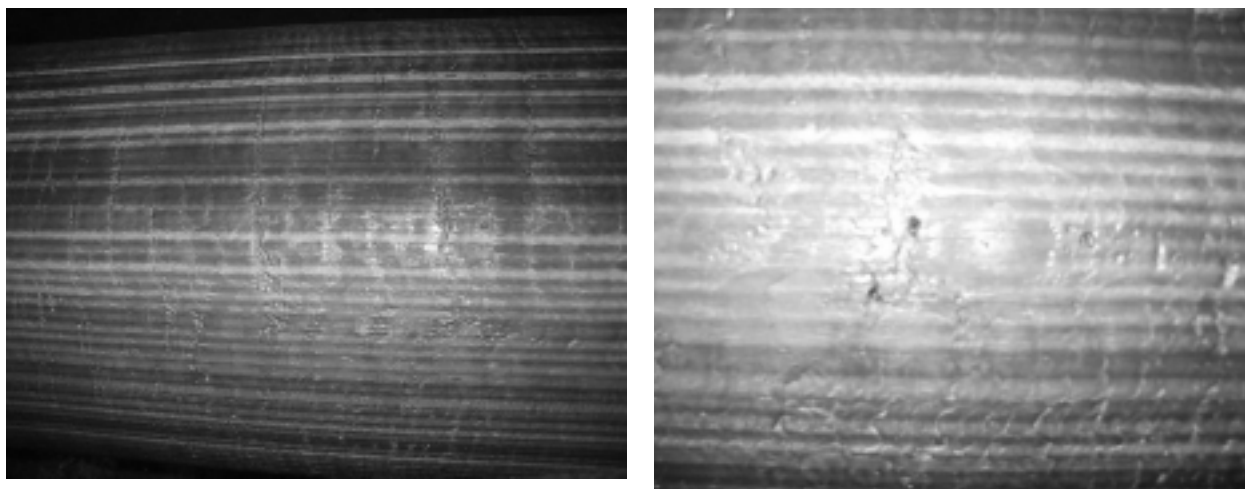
Надрывы, складчатость и поперечные трещины на поверхности чернового слитка
